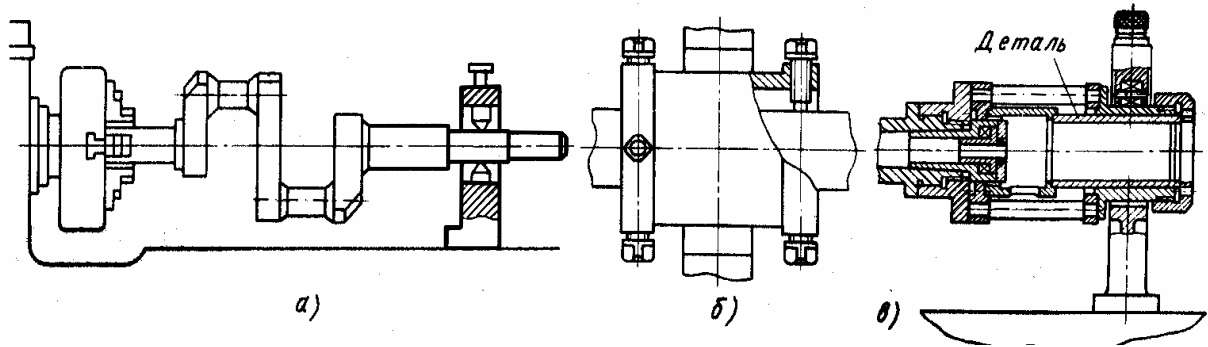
Схеми установлення заготовок в патроні та на нерухомому люнеті
